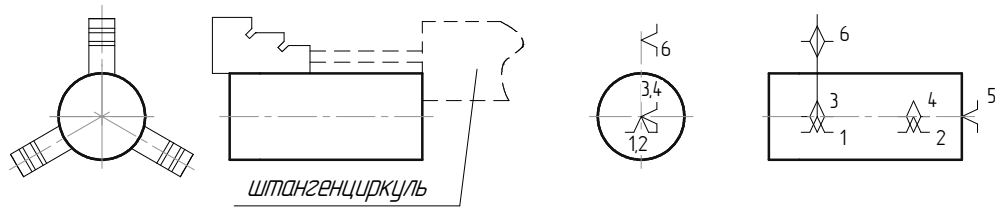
Схема базування вала у трикулачковому самоцентрувальному патроні.
